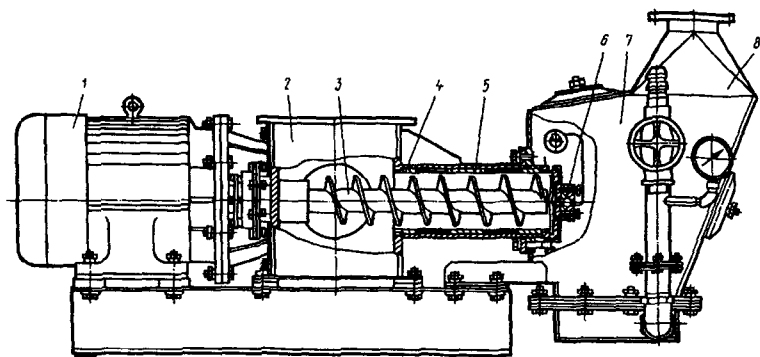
Пневмовинтовой насос: 1 – двигатель; 2 – загрузочная воронка; 3 – винт; 4 – гильза; 5 – корпус; 6 – клапан; 7 – смесительная камера; 8 – трубопровод.
